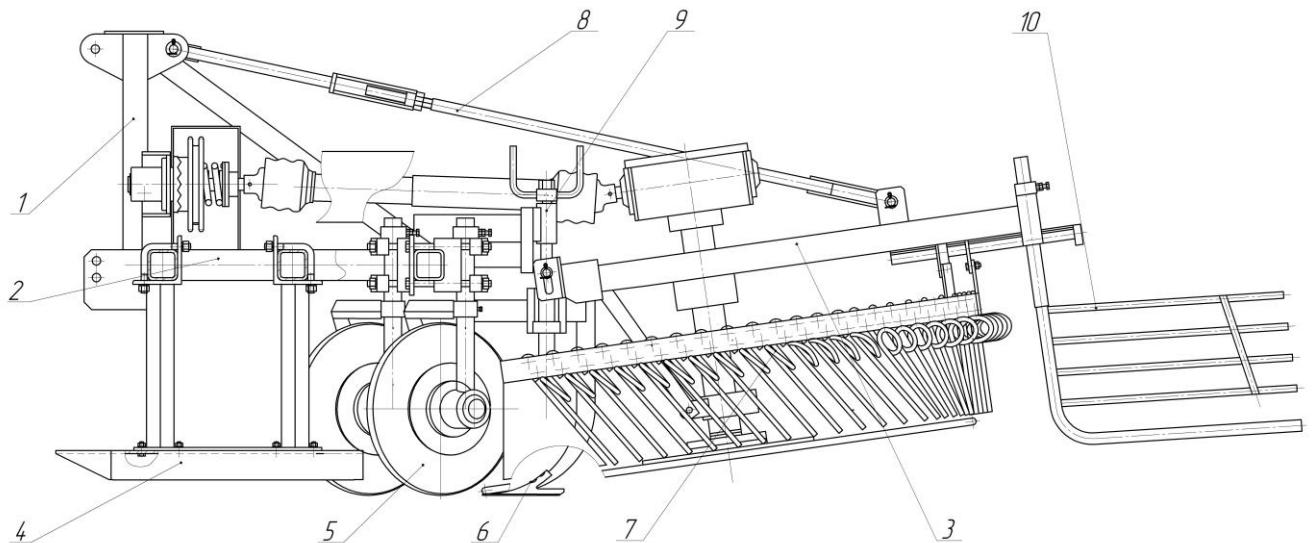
Схематичне зображення бурякозбирального агрегату АЗБ-6 (вигляд збоку): 1 – начіпний пристрій; 2 – передня рама; 3 – задня рама; 4 – лижа; 5 – викопуючий диск; 6 – розпушувальна лапа; 7 – бокова решітка з пружинних пальців; 8 – телескопічна тяга; 9 – гвинтовий регулюючий механізм; 10 - валкоутворювач
